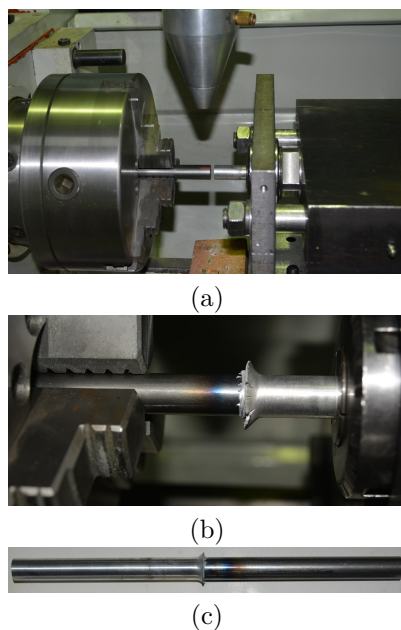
Proceso de soldadura. a) Aplicación láser sobre el eje de acero. b) Formación del flash en el eje de aluminio. c) Probeta soldada
